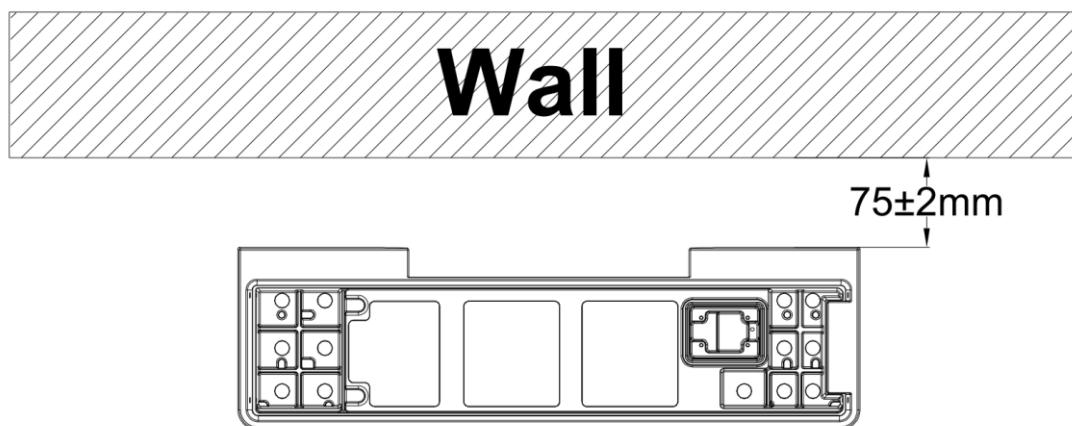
Draufsicht auf die Sockelmontage
